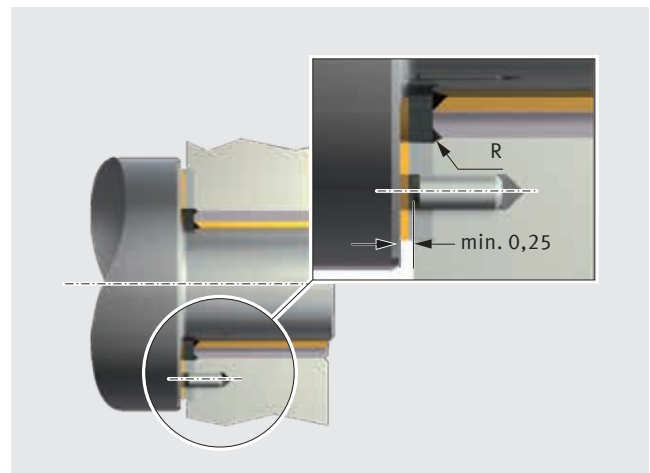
Befestigen einer Anlaufscheibe PAW in einer Ausnehmung im Gehäuse
